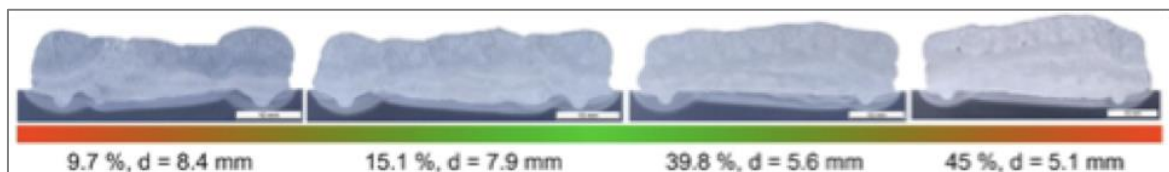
Parametre seti 25–2 için farklı kaynak dikişi bindirmeleri/boncuk mesafeleri için makro kesitler [15]
